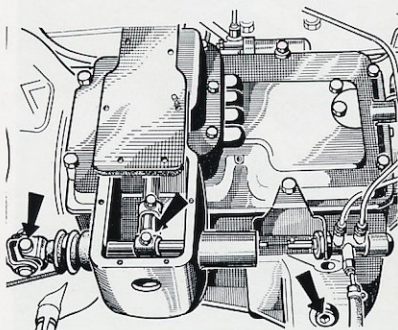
Entretien et graissage du boîtier à rotule du changement de vitesses (Boîte B 151) et de la tringlerie de commande sur cabine avancée.
